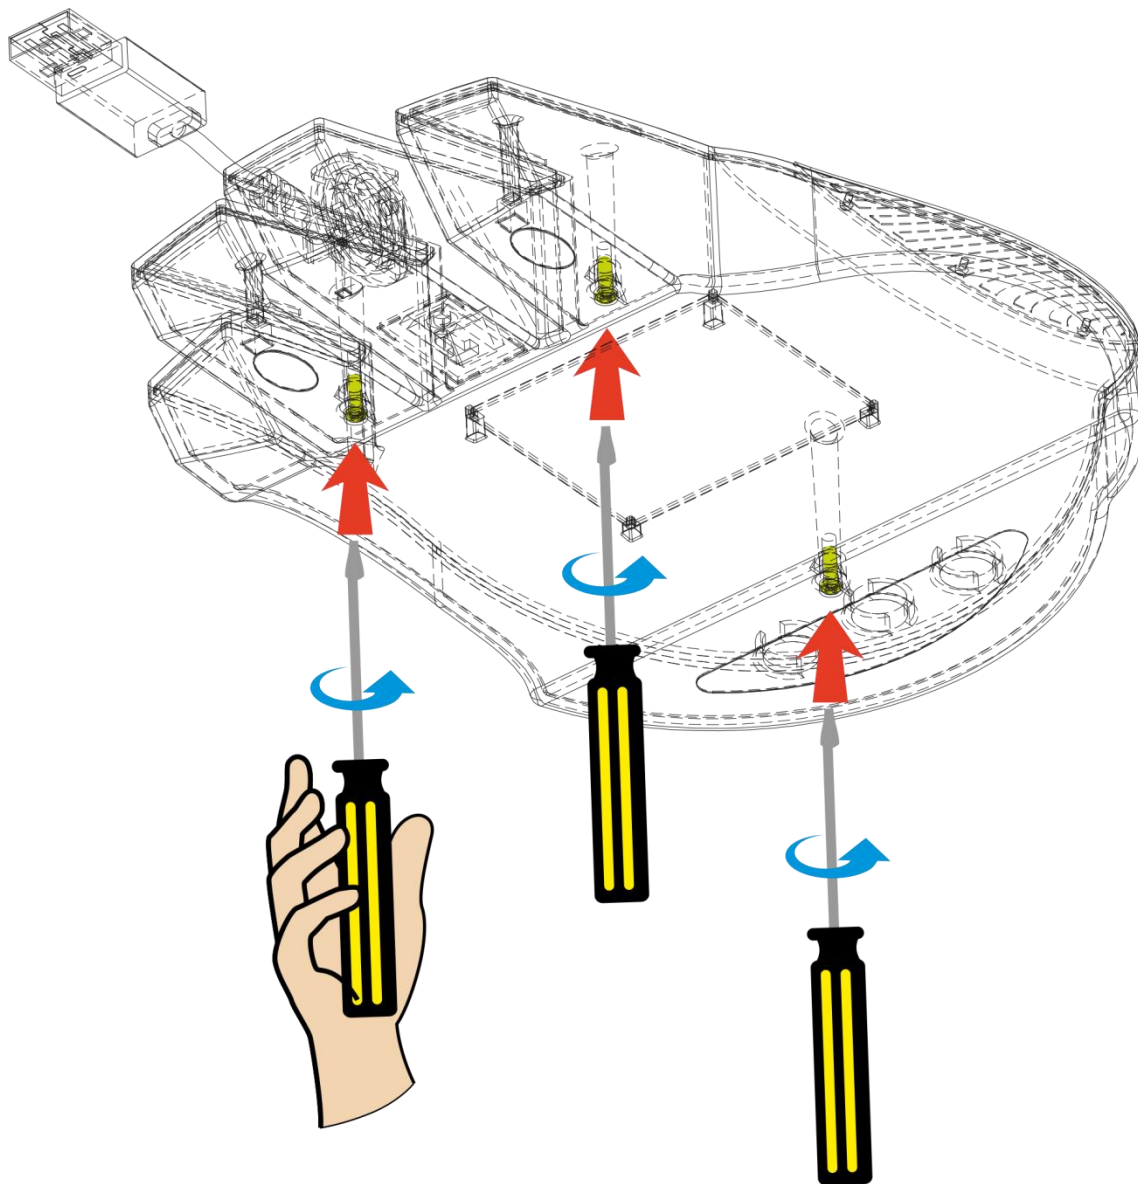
Ensamblaje 2 – 1 (3)
